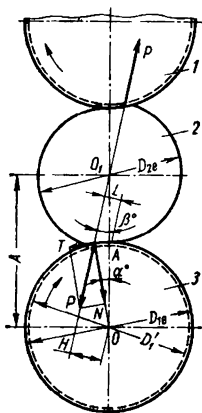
Схема действия сил при накатке шестерни: 1 — валок; 2 — валок; 3 — заготовка;
